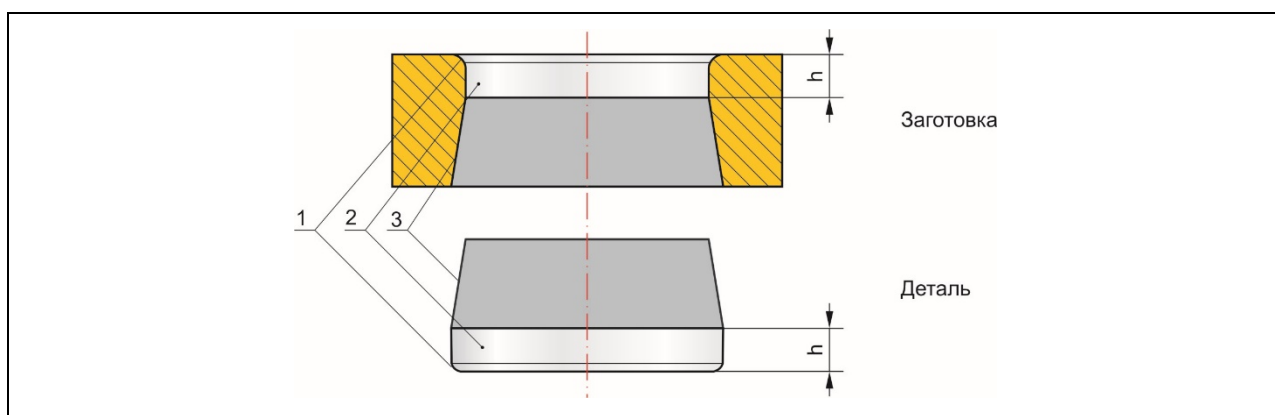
Характерные участки боковой поверхности детали и заготовки после вырубки
